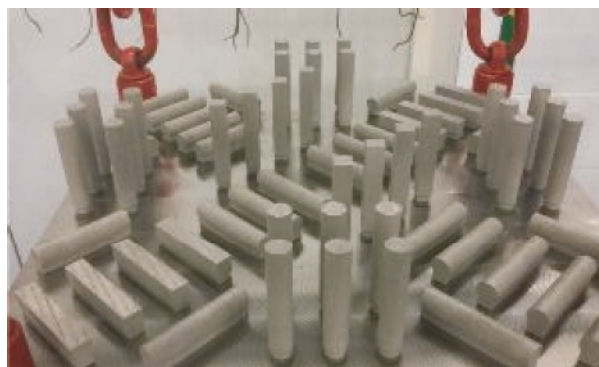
Платформа построения с расположенными на ней образцами, изготовленными селективным лазерным сплавлением в направлении XY и Z
